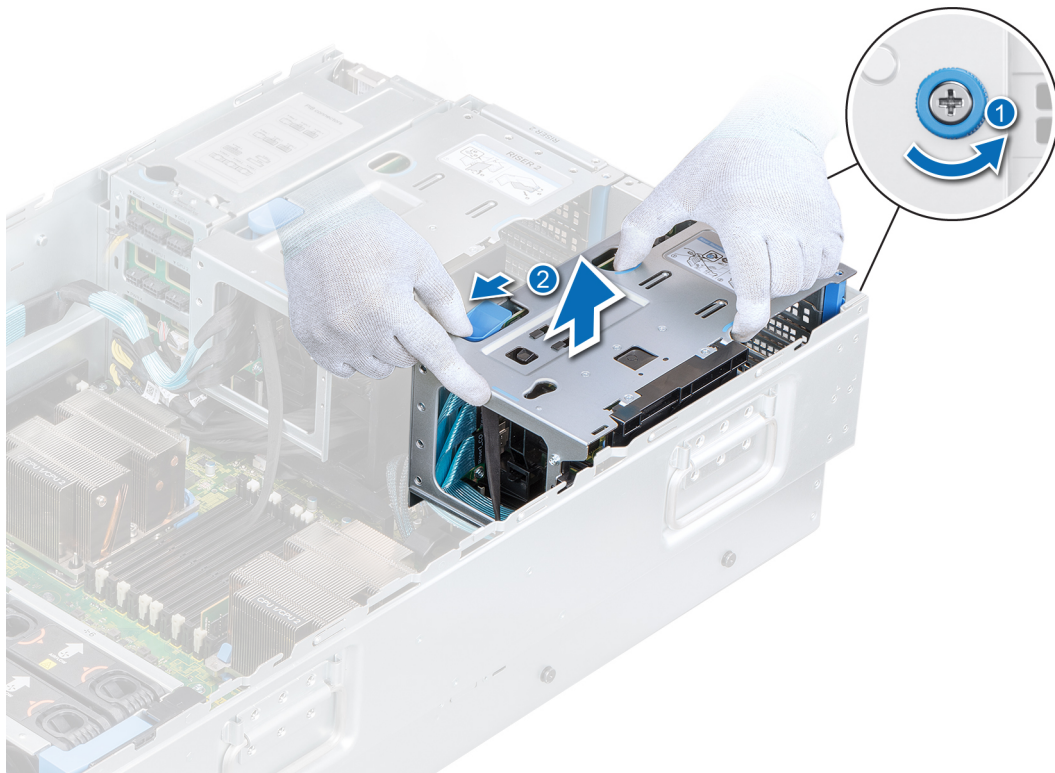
Entfernen von PCIe-x8-Riser 1
